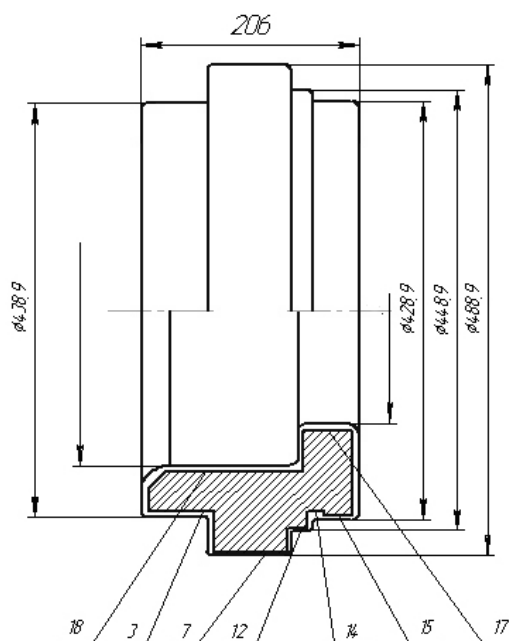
Совмещенный чертеж детали с заготовкой
